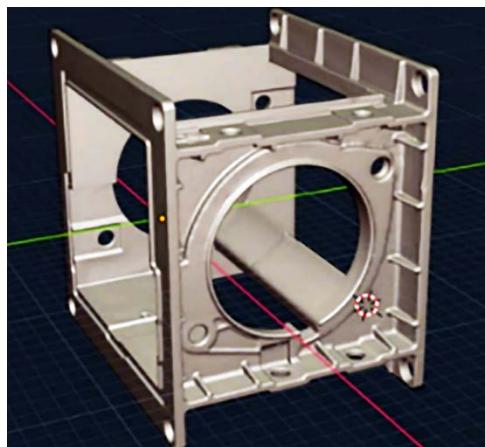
3D-модель корпуса дозатора HORSCH PP
